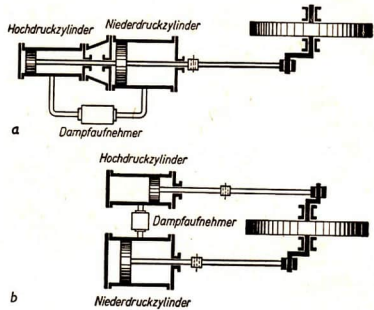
Die gebräuchlichsten Formen der Mehrzylindermaschine
